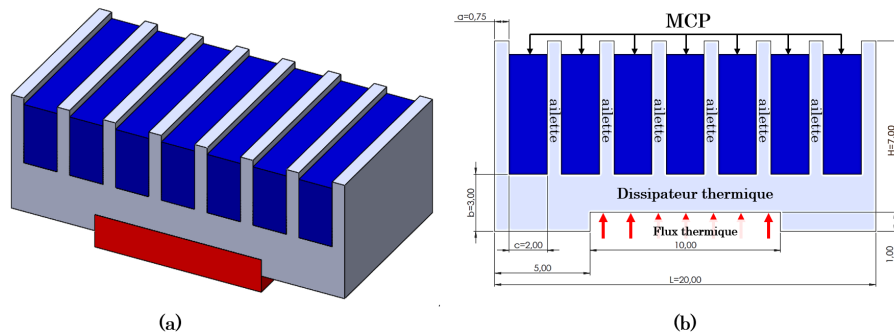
Modèle du dissipateur thermique à base du MCP (a) : assemblage 3D et (b) : géométrie et dimensions
